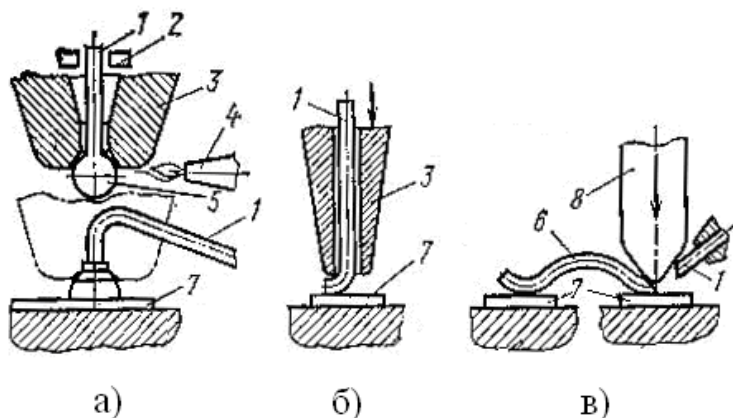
Разновидности термокомпрессионной сварки:
